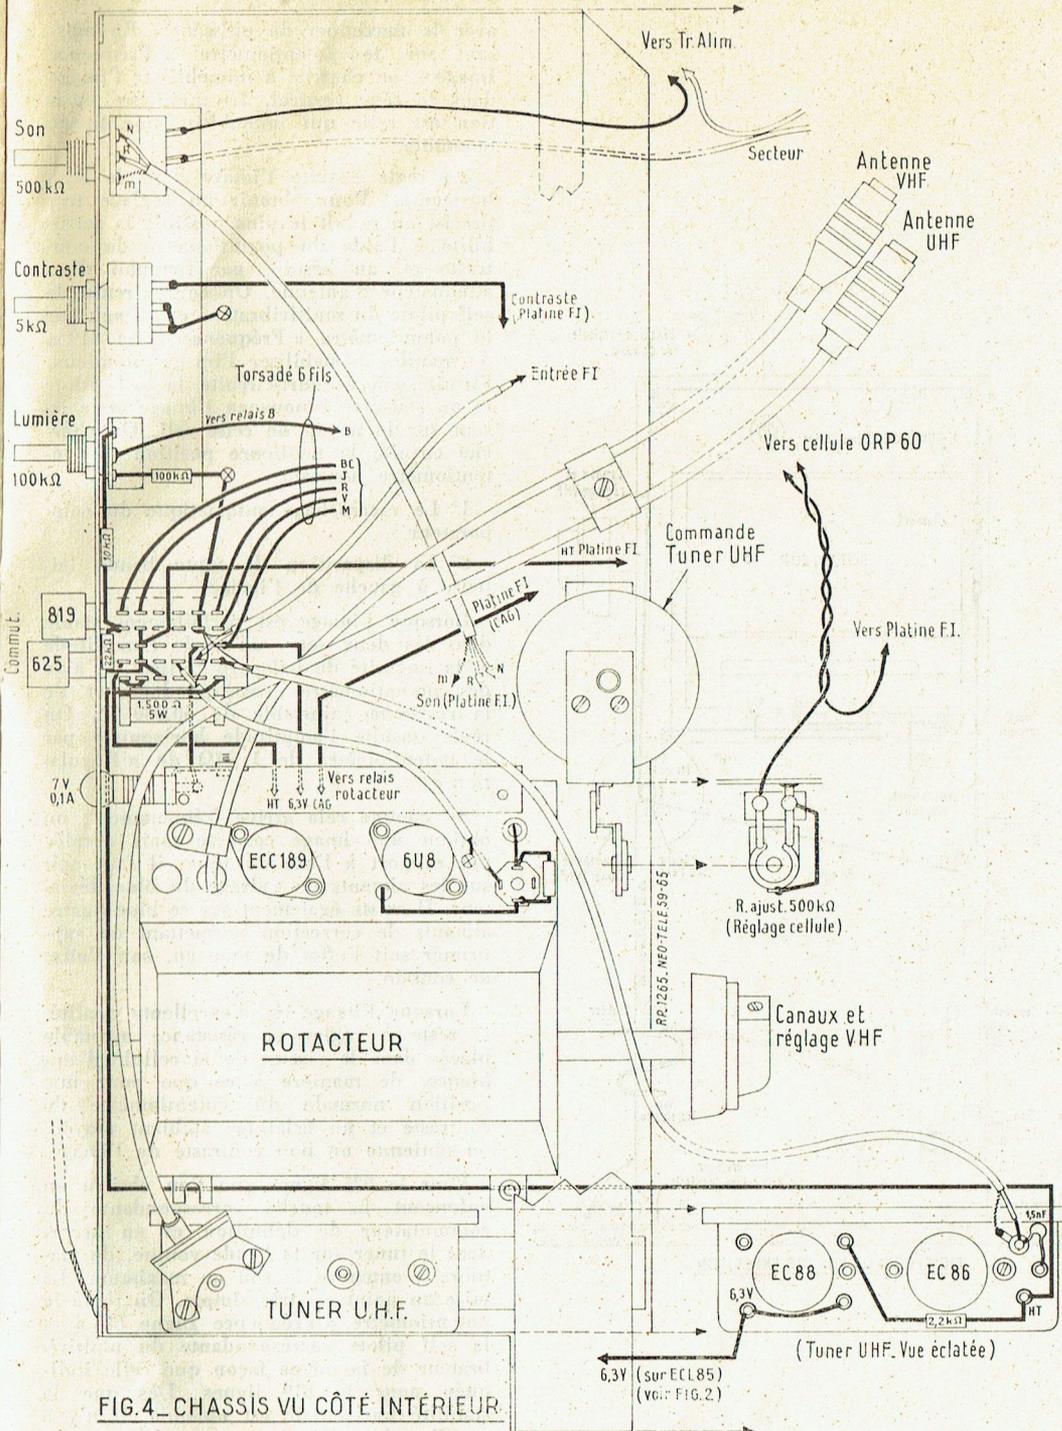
CHASSIS VU CÔTÉ INTÉRIEUR.
